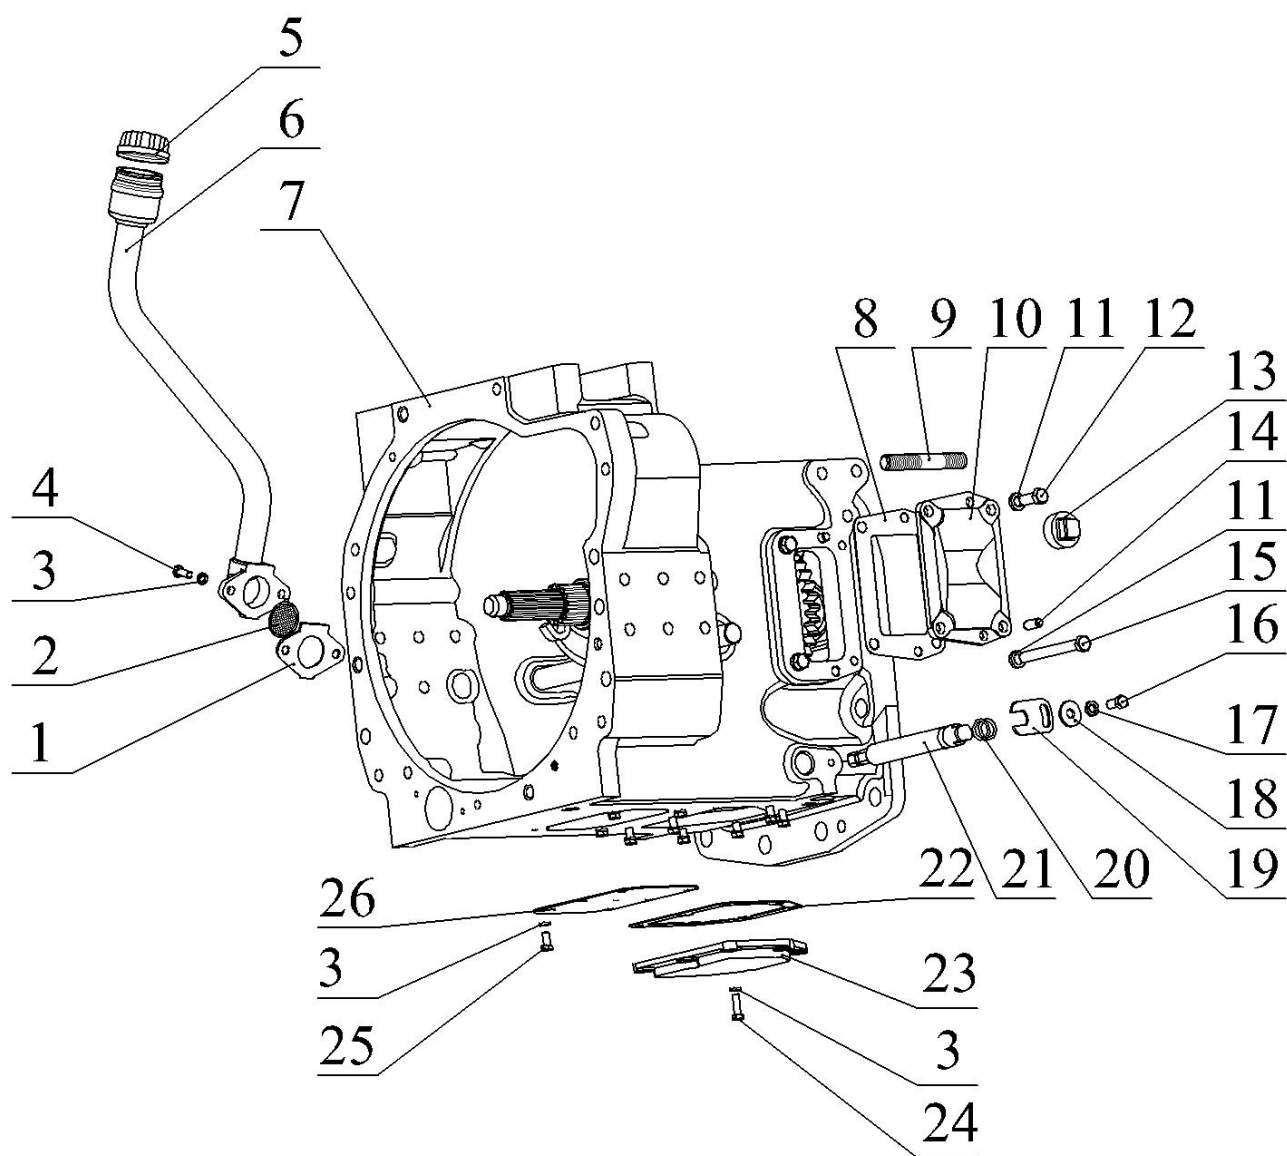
Корпус сцепления (лист 1 из 3)
